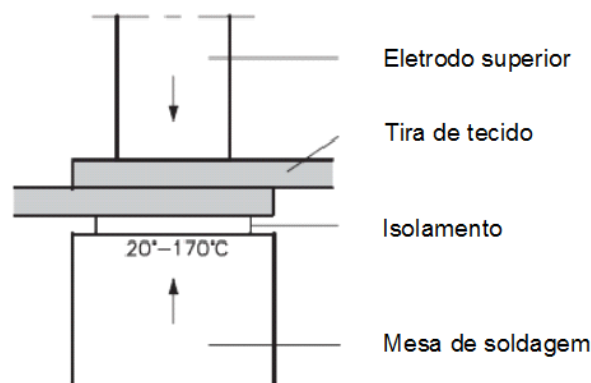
Processo de soldadura por alta frequência [2].
